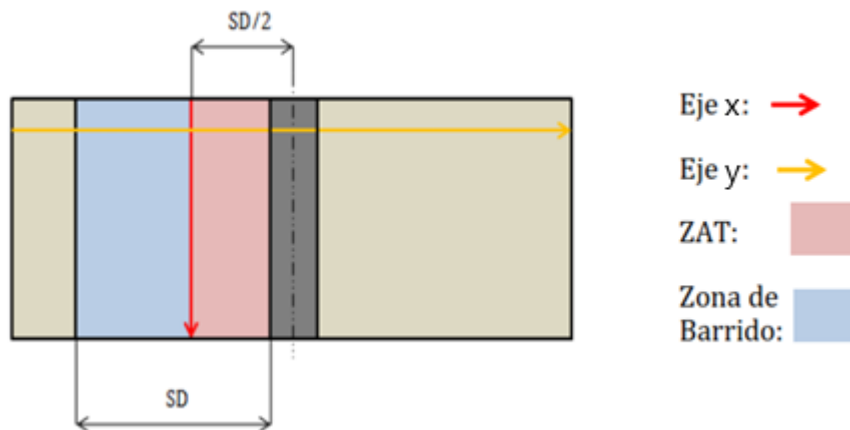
Marcado de la placa soldada a tope.
